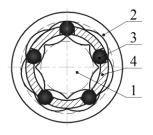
Зубчатая передача с промежуточными телами качения и параллельными осями: 1) зубчатое колесо; 2) зубчатое колесо; 3) промежуточное тела качения; 4) сепаратор
